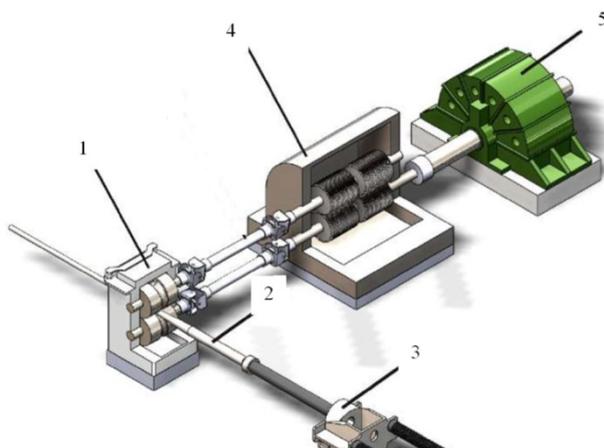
Функциональная модель пилигримового стана: 1- прокатная клет, 2- заготовка для трубы, 3- механизм подачи, 4- двухвалковая шестеренчатая клет, 5- приводной двигатель.
